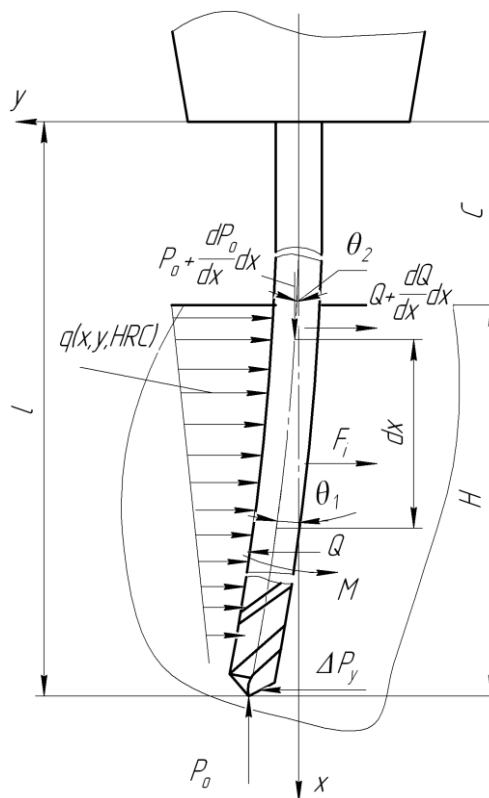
Розрахункова схема для визначення коливань свердла в процесі свердління отвору [22]
